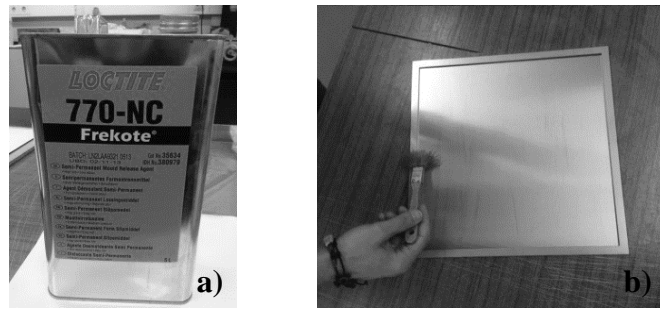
a) Desmoldante Loctite® - Frekote 770-NC™; b) Aplicação do desmoldante no molde.
